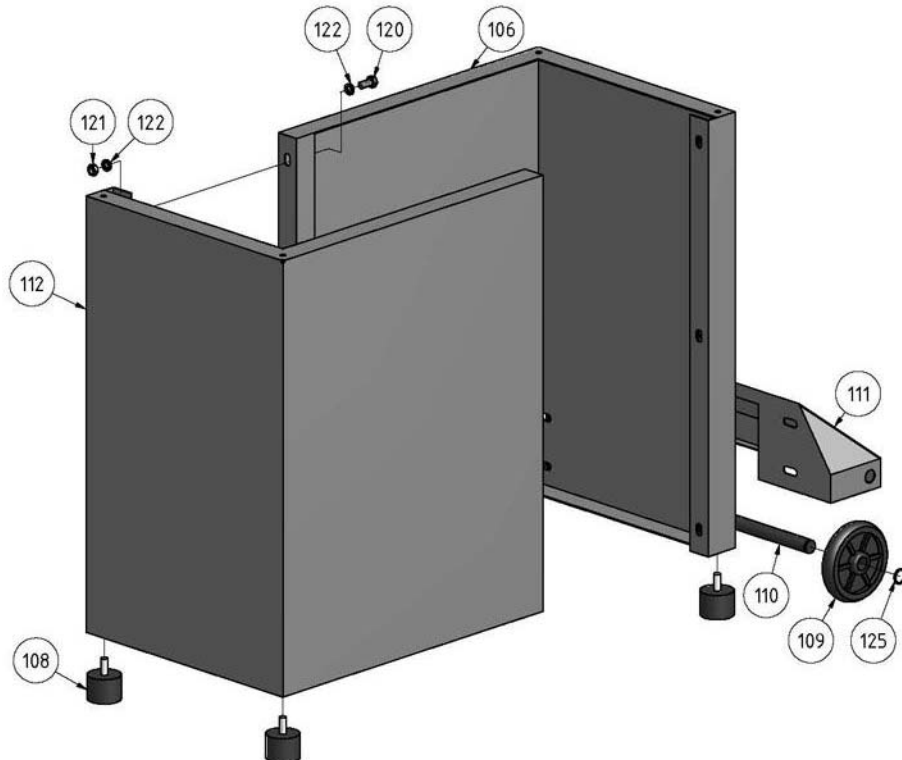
Ersatzteilzeichnung 4 von 4 - Parts drawing 4 of 4
